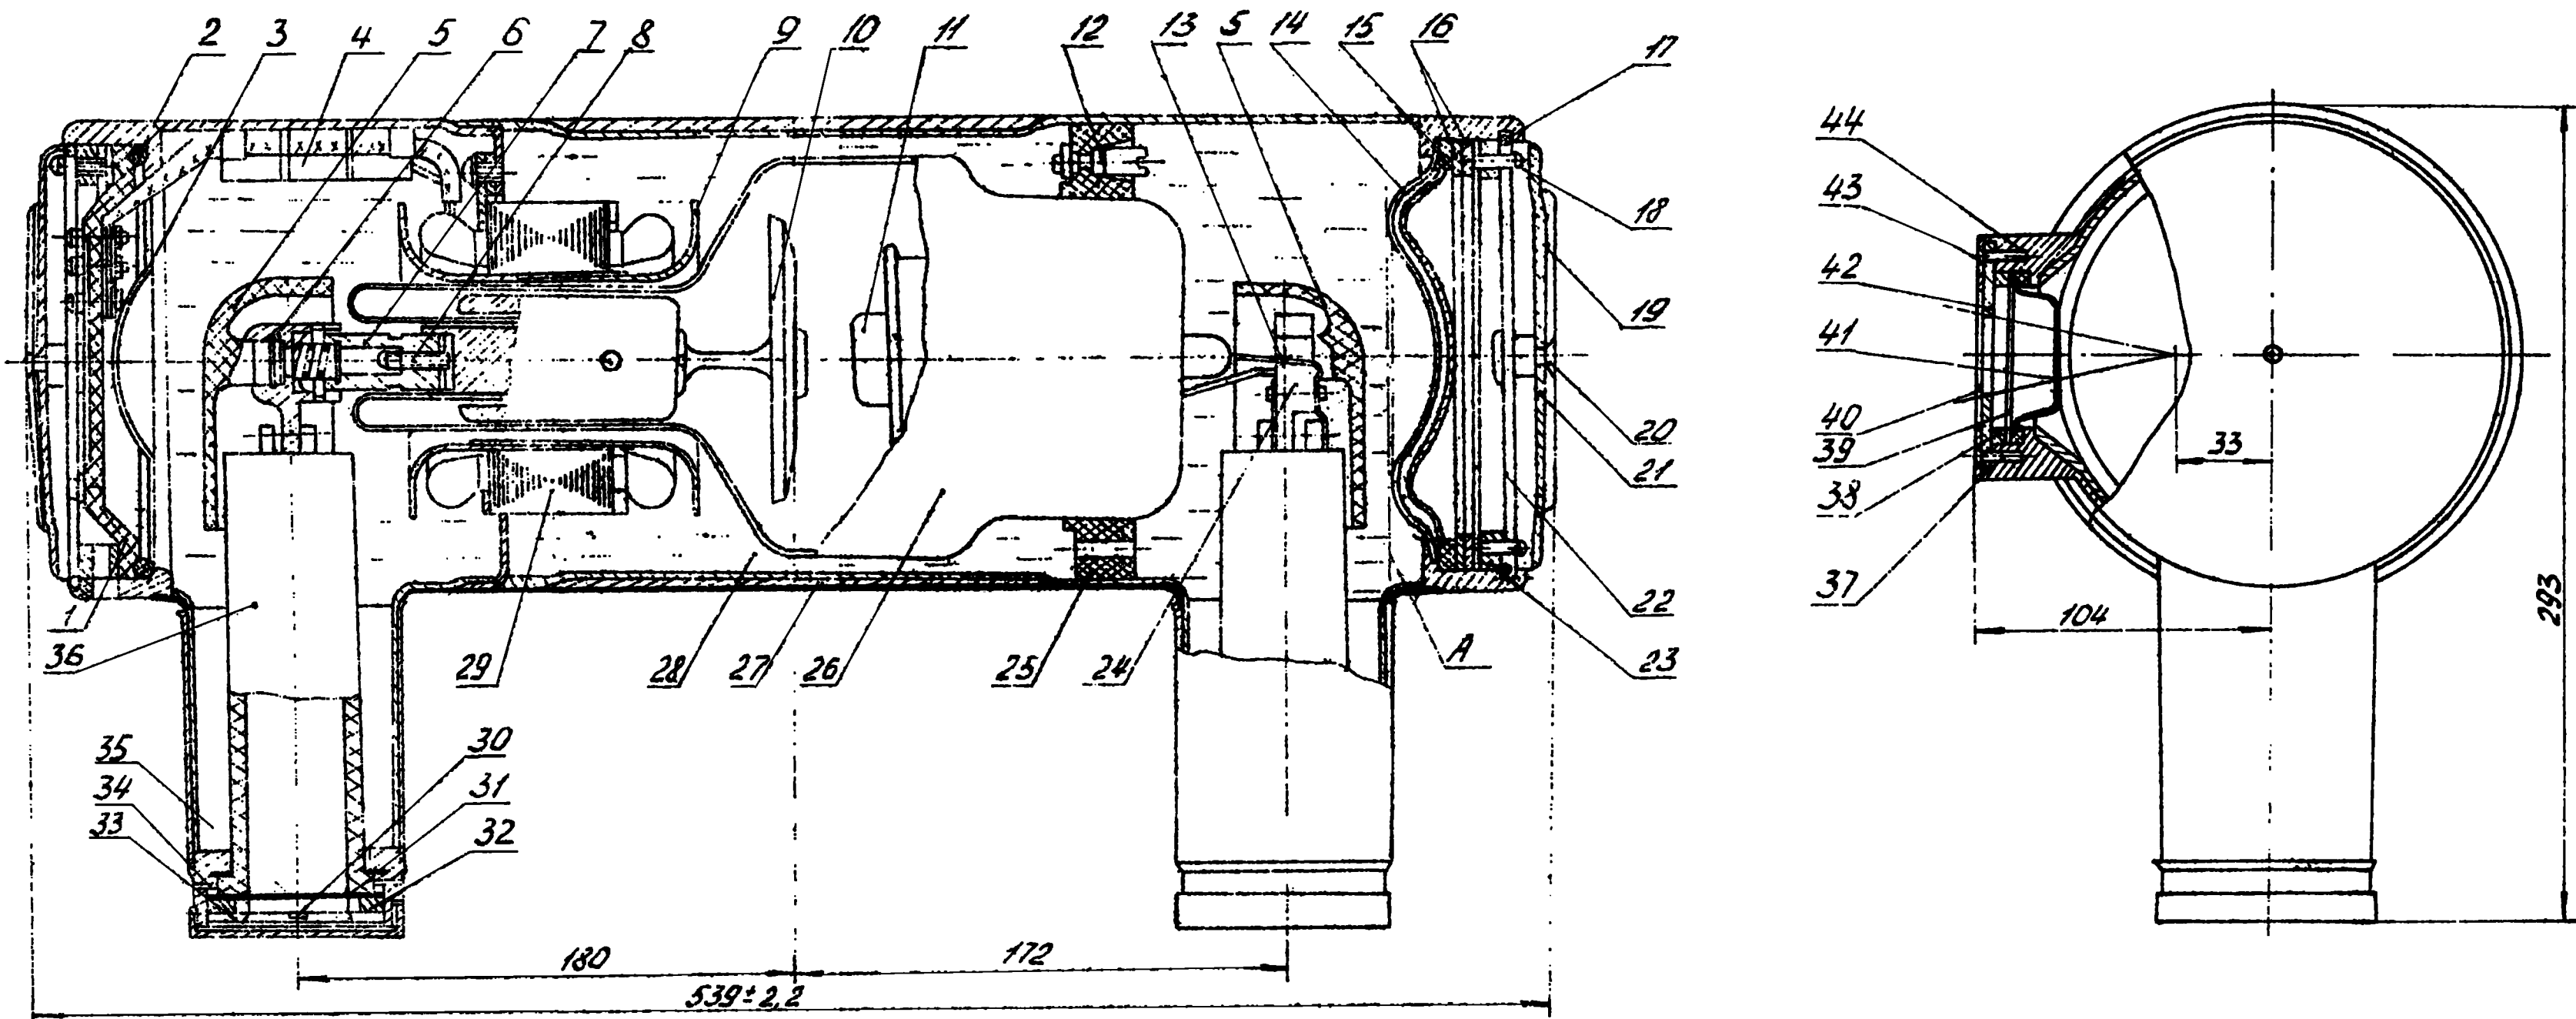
Излучатель рентгеновский. Сборочный чертеж.
